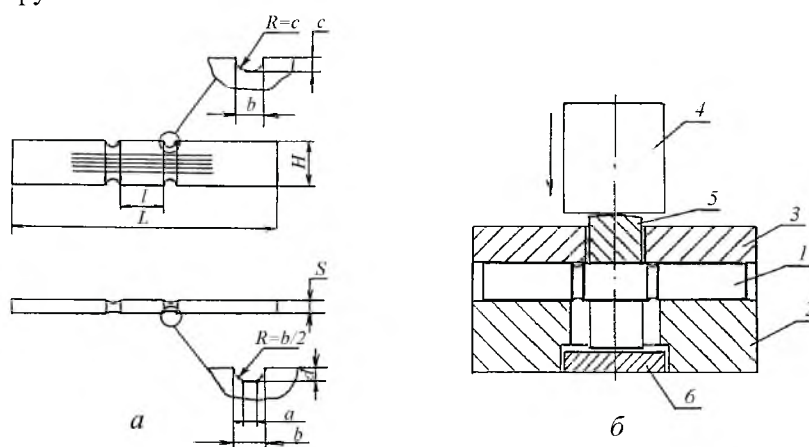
Плоский образец для испытаний на сдвиг (а) и схема его нагружения (б).
